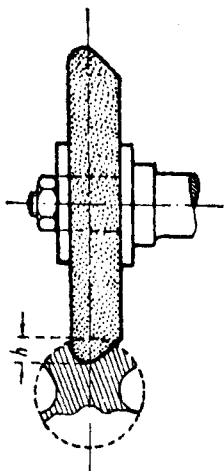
Профиль шлифовального круга для шлифовки канавок метчика.
